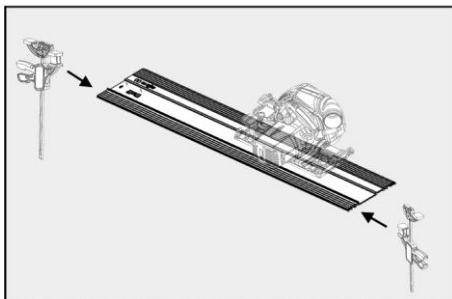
Fissaggio del pezzo con morsa di serraggio
